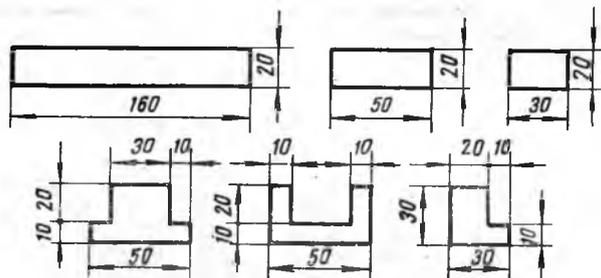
Форма и размеры сечений фигурных деталей из измельченной древесины
